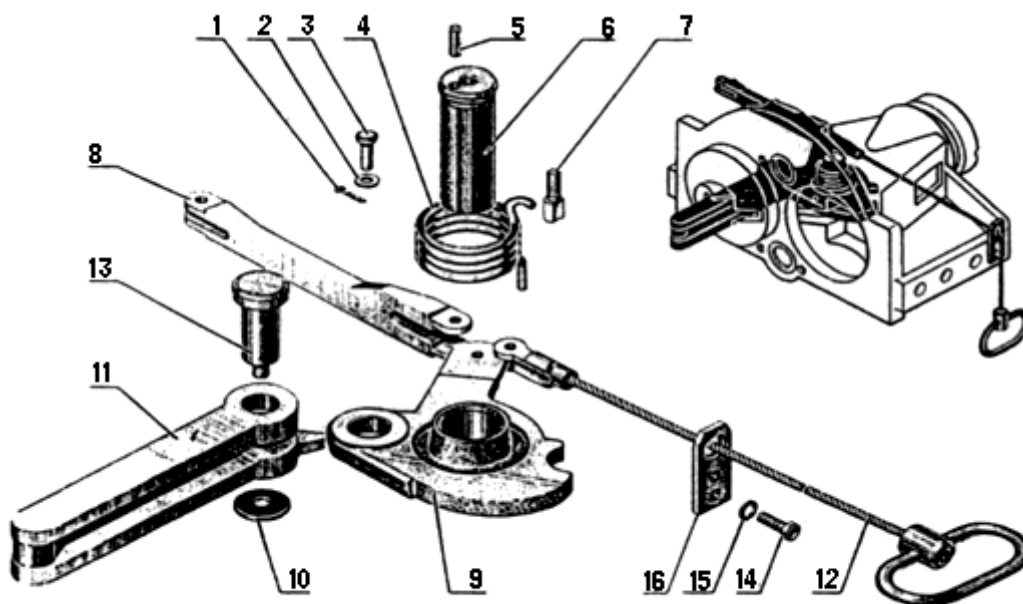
Деталі зчіпного механізму автозчепу:
